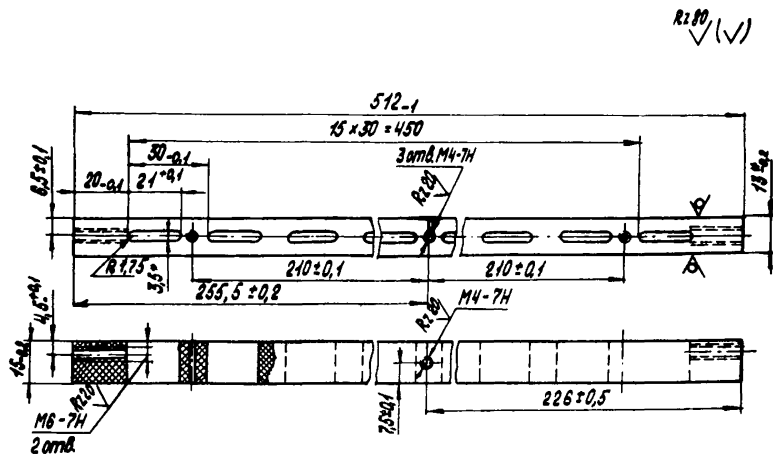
Планка кассеты для установки контрольных образцов через байпас.
